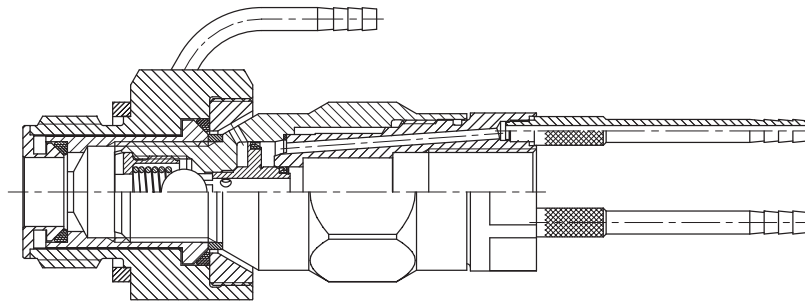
Zweiweg-Umschaltadapter Typ 737 im Adapter Typ 7511
